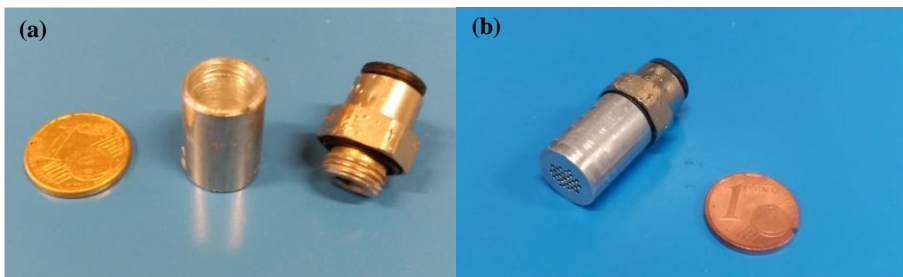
(a) Cilindro de aluminio mecanizado con rosca y adaptador tubo a rosca. (b) Detalle de ambas partes unidas donde se aprecia la rejilla de extracción.
